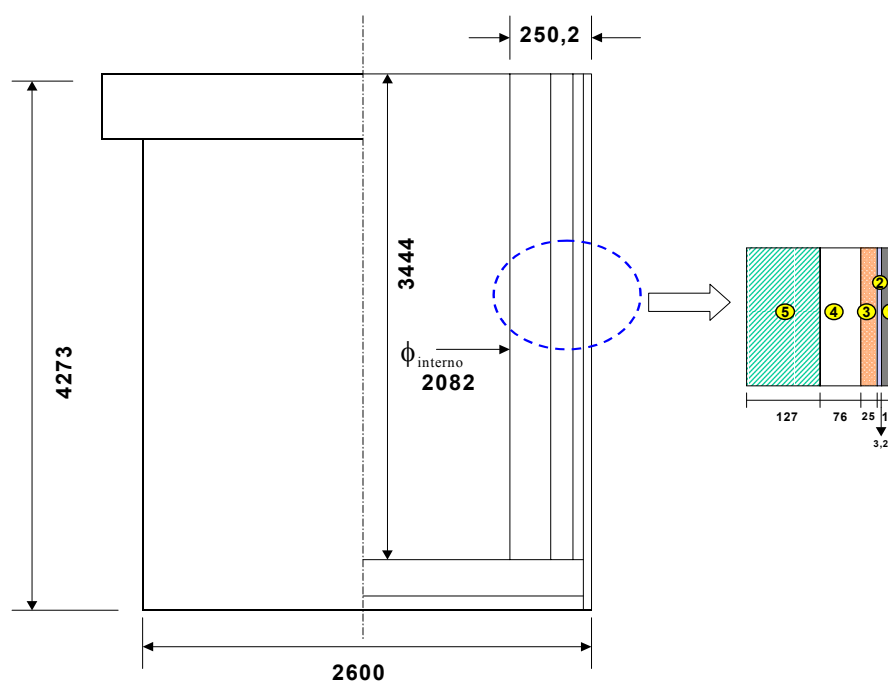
Desenho esquemático da parede e detalhe da disposição do refratário.
